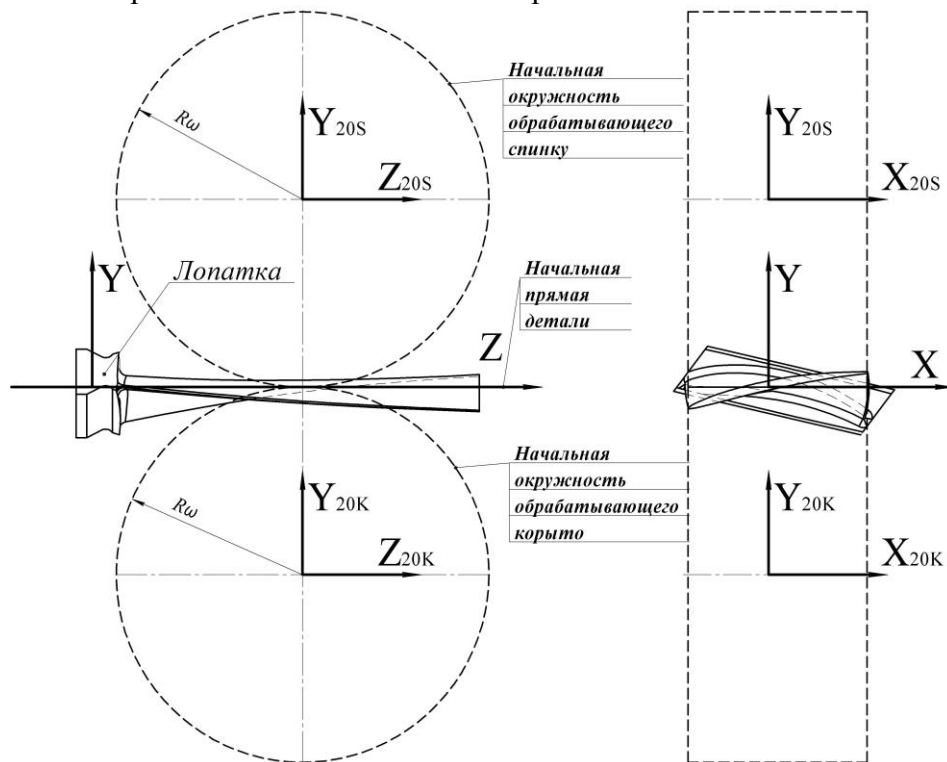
Общая схема расчета координат профиля валков об обработке поверхности лопаток.
